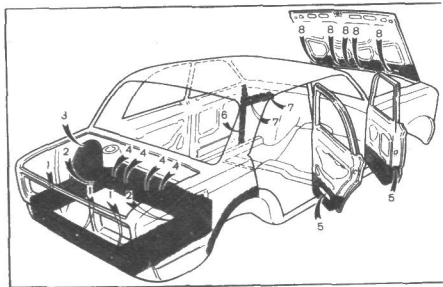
Скрытые полости кузова (вид справа): 1 — нижняя поперечина задка; 2 — лонжероны пола задка; 3 — задние крылья; 4 — поперечина заднего пола; 5 — карманы дверей; 6 — передние стойки; 7 — соединители боковины и щитка передка; 8 — карманы капота
